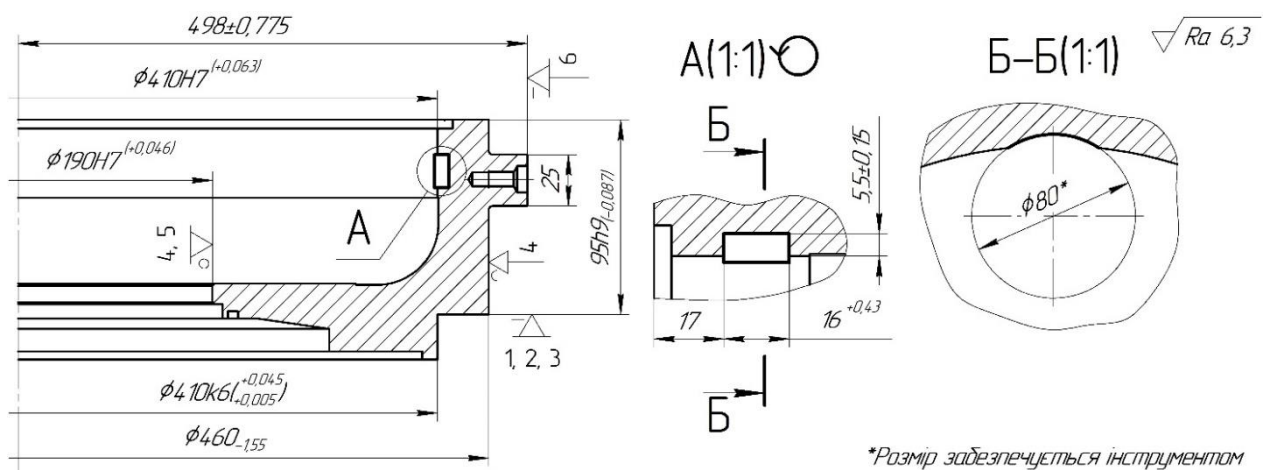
Ескіз заготовки на операції 035. Установ А
